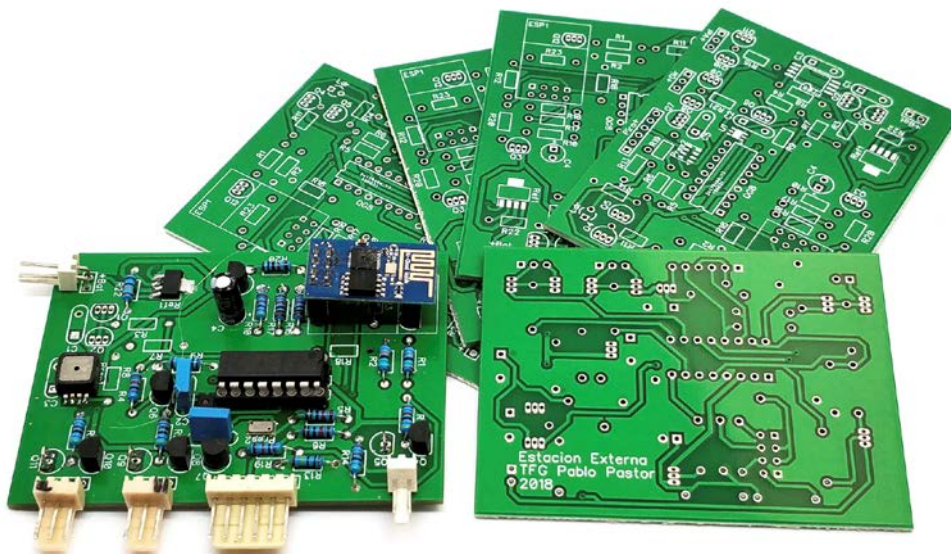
Conjunto de las PCB disponibles para su futura instalación
